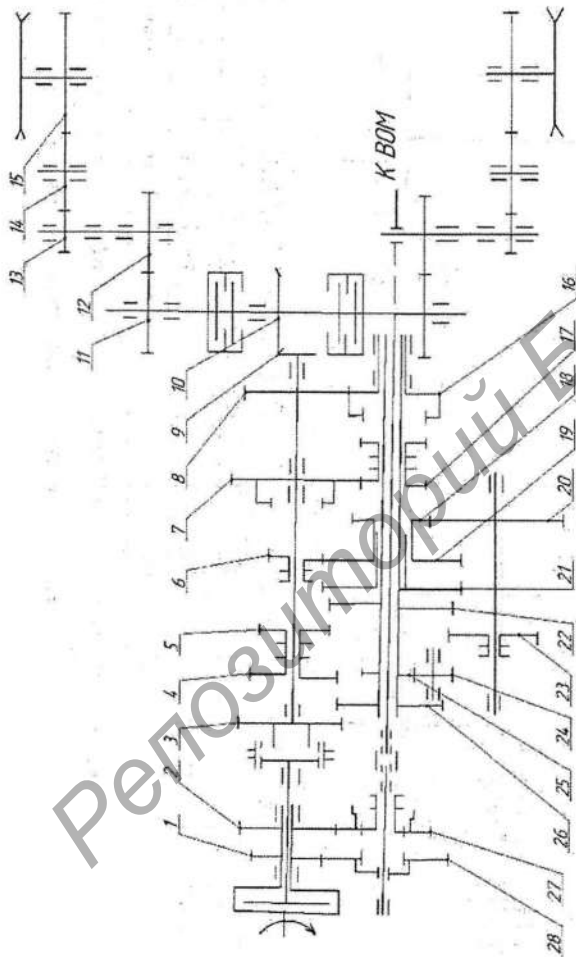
Кинематическая схема силовой передачи трактора Т-150К [30]
